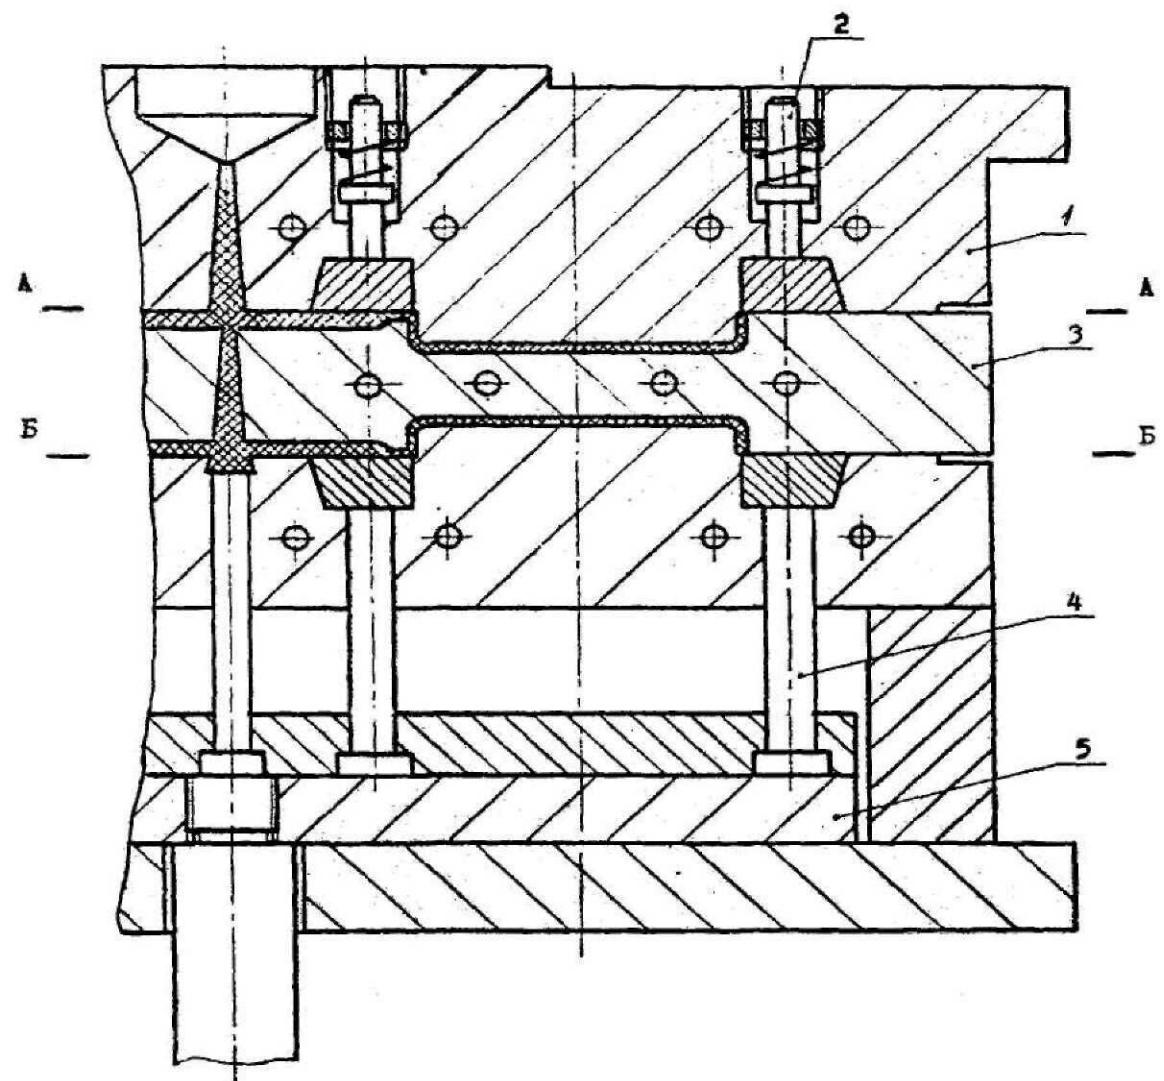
Пресс-форма для изготовления простых деталей небольшой высоты:
